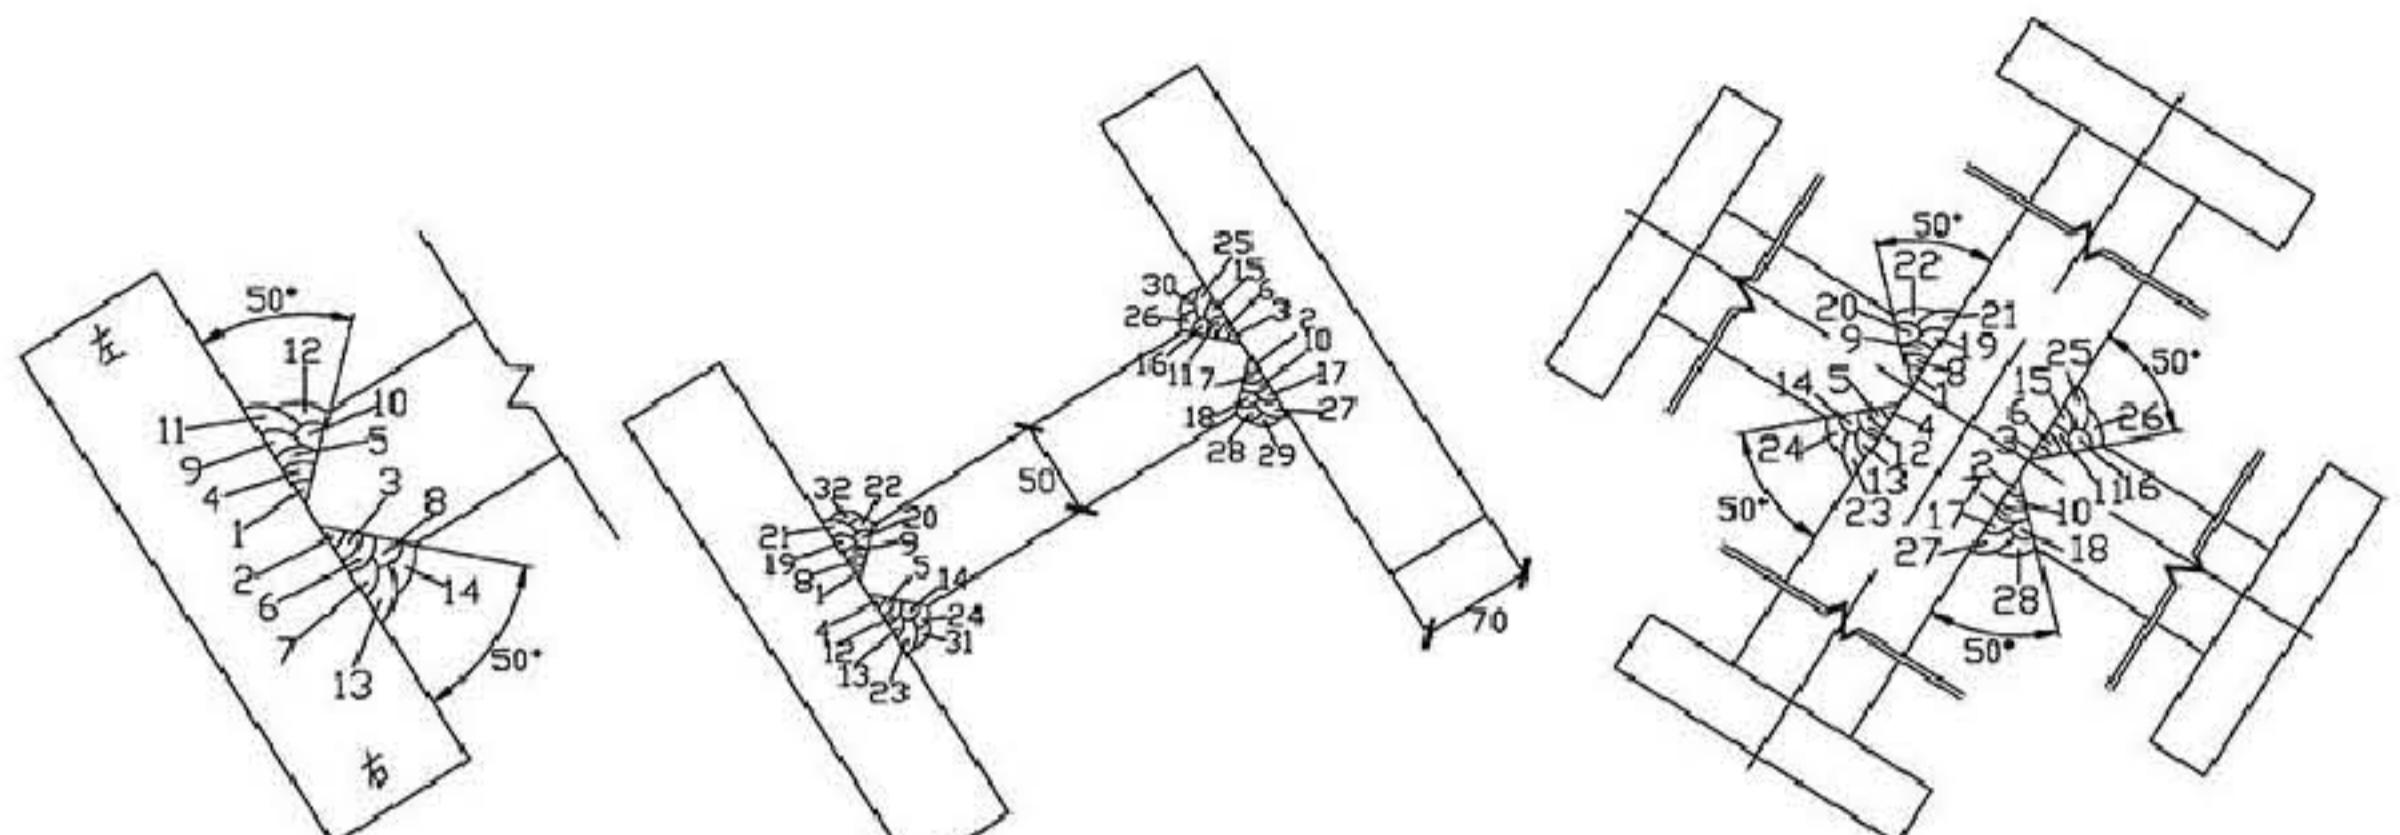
T 形、H 形、十字形柱焊接顺序
